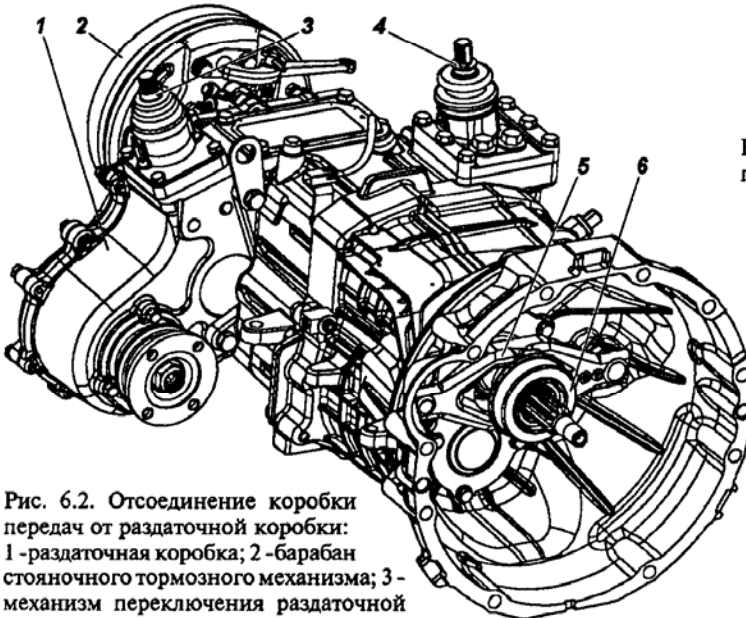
Отсоединение коробки передач от раздаточной коробки: 1 -раздаточная коробка; 2 -барабан стояночного тормозного механизма; 3 - механизм переключения раздаточной коробки; 4 -механизм переключения коробки передач; 5 -вилка подшипника выключения сцепления; 6 -подшипник выключения сцепления
